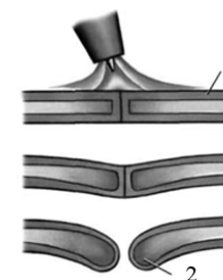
Несплавление кромок алюминиевых конструкций:
